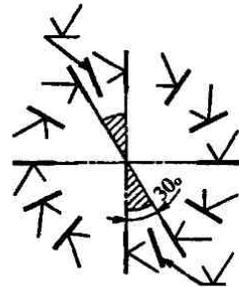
Обозначения шероховатости поверхностей, знак которых без полки
